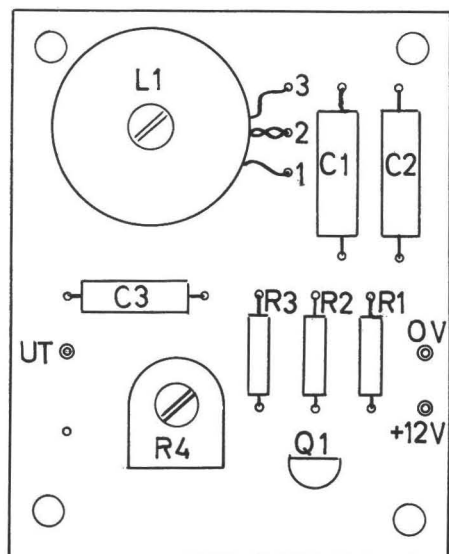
Komponentplacering för tongeneratoren. Plattans storlek 50x30 mm.
